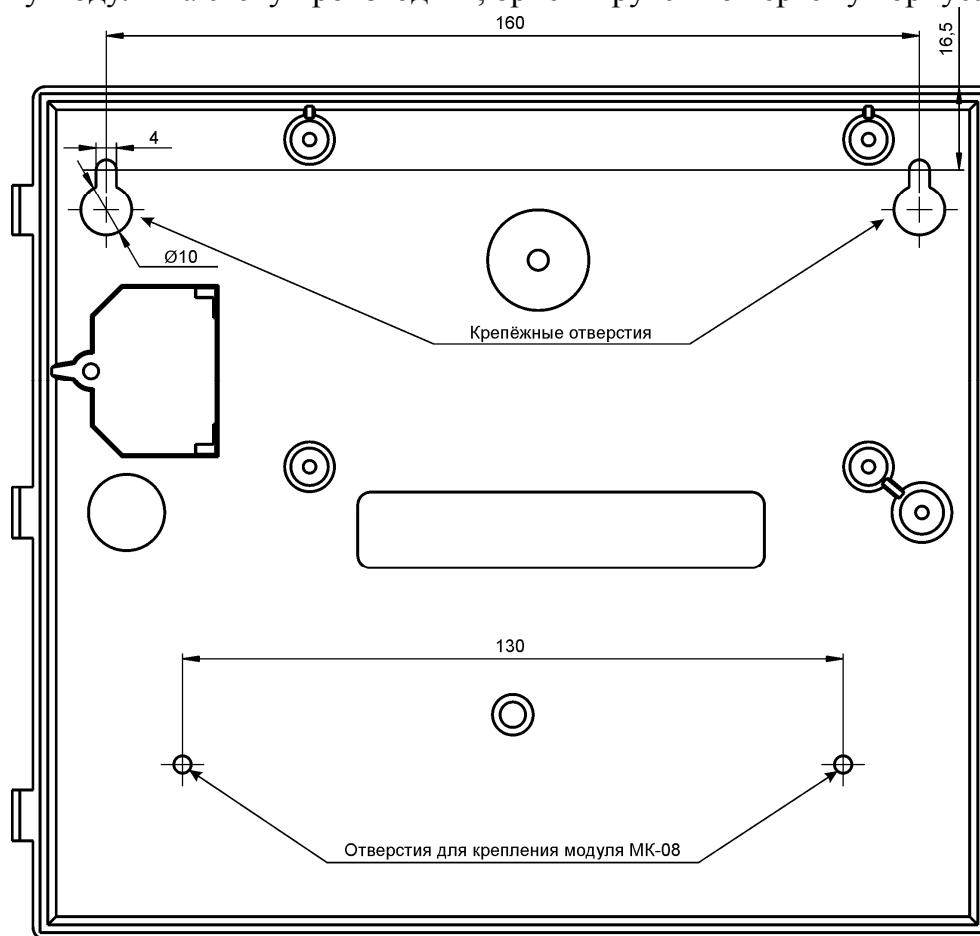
Установочный чертёж корпуса (вид изнутри)
